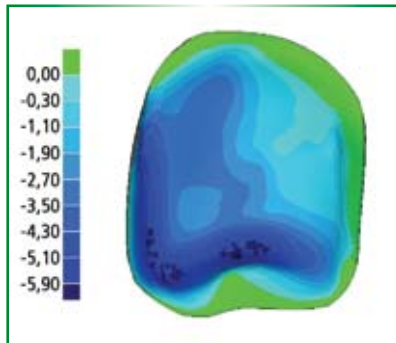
Diferenças, em milímetros, entre o implante projetado e o implante conformado por estampagem incremental
